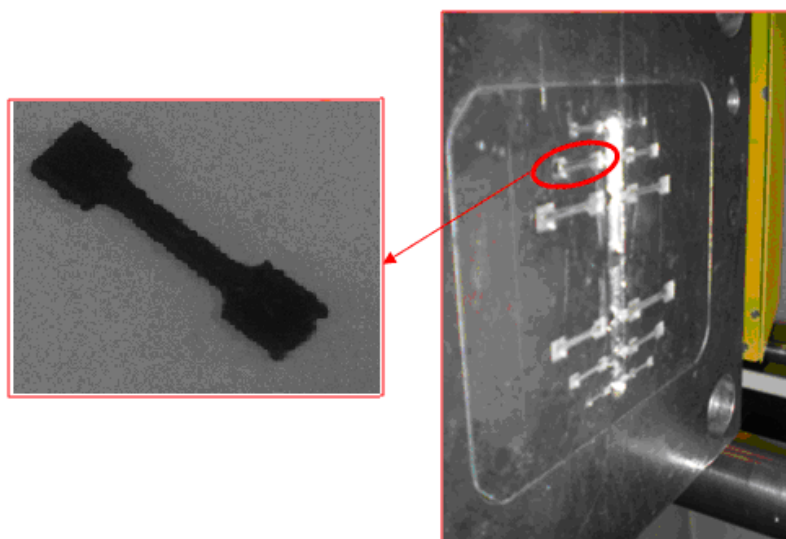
Epreuves de traction obtenues par moulage par injection en utilisant un moule multi-empreintes.
